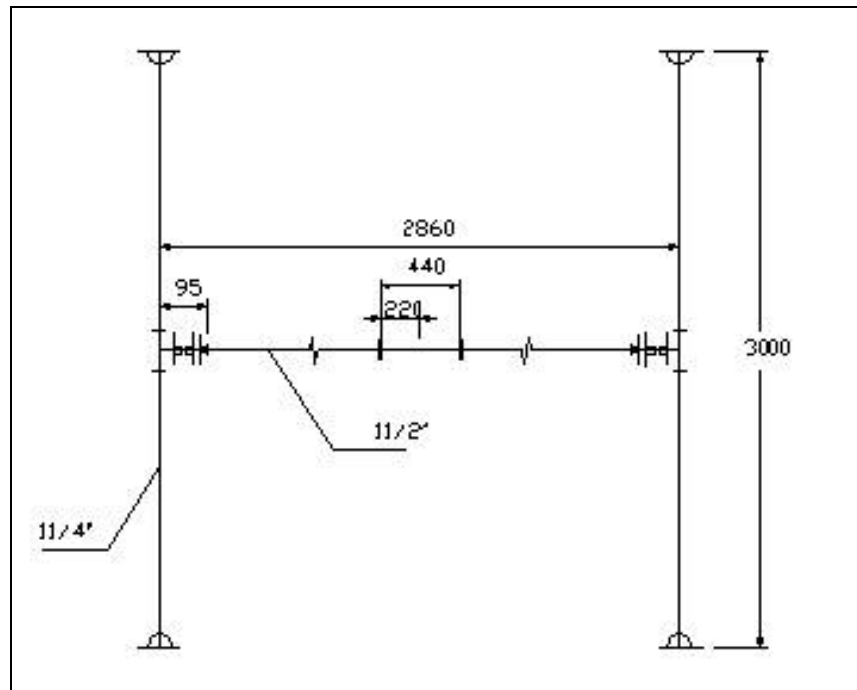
Desenho representativo das dimensões da Estrutura H.
